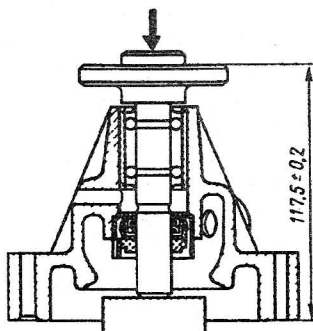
Напрессовка ступицы шкива водяного насоса на вал
